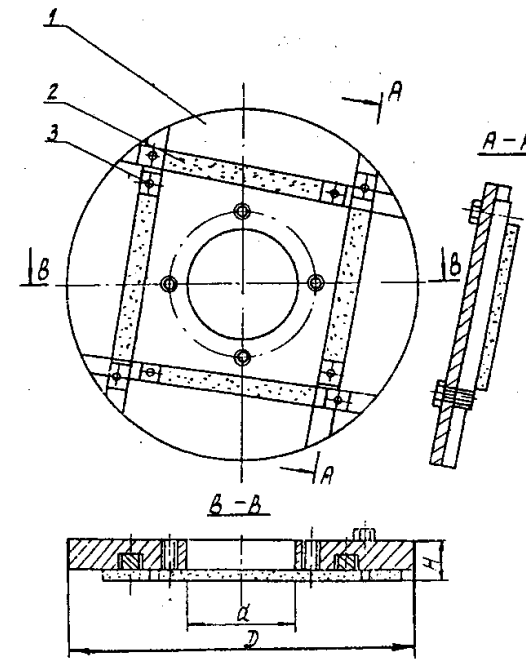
Торцевая алмазная фреза АПС-2 (планшайба): 1 — корпус фрезы; 2 — алмазосодержащий элемент; 3 — крепежные элементы
